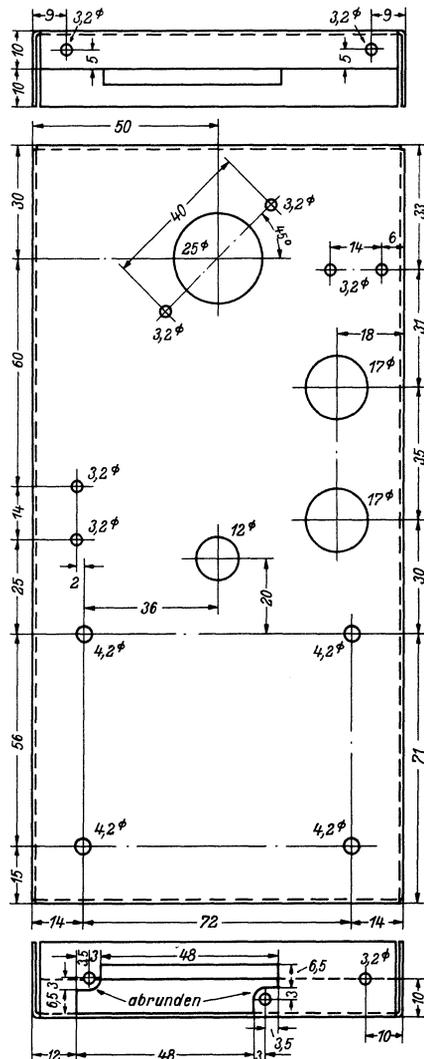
Das Chassis des Gerätes (1-mm-Eisenblech)
